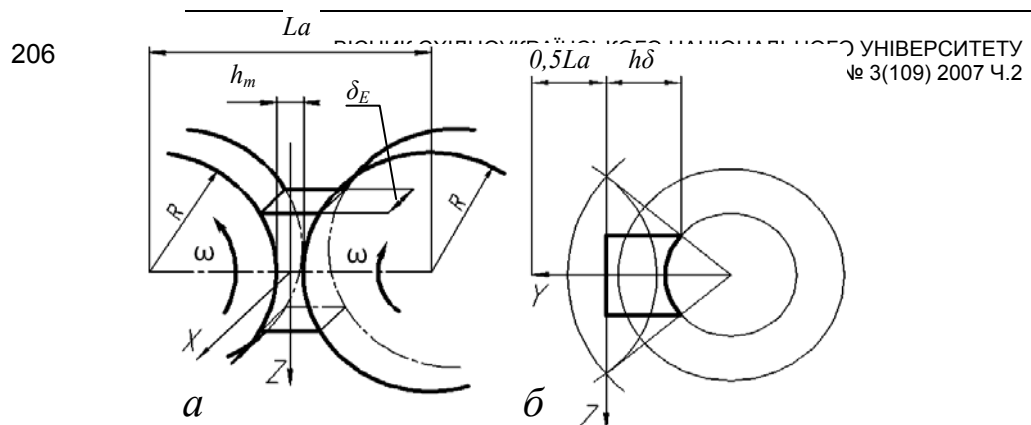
Радиальный (а) и боковой (б) зазоры в зацеплении червяков двухчервячного прессы
